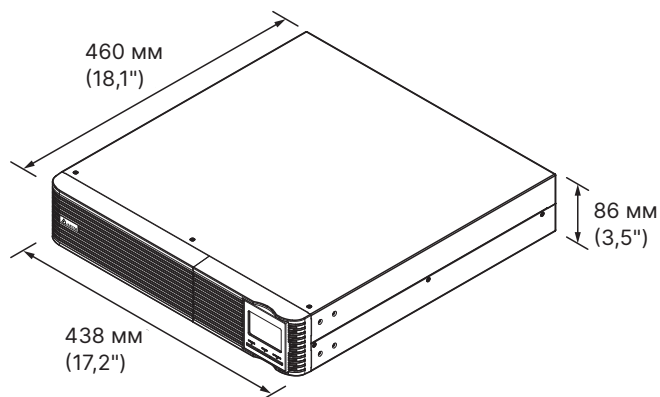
Внешний вид и размеры_ 2 кВА)
